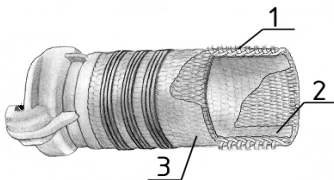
Конструкция латексированного рукава: 1 – армирующий каркас; 2 – внутренний гидроизоляционный слой; 3 – наружная латексная пленка
